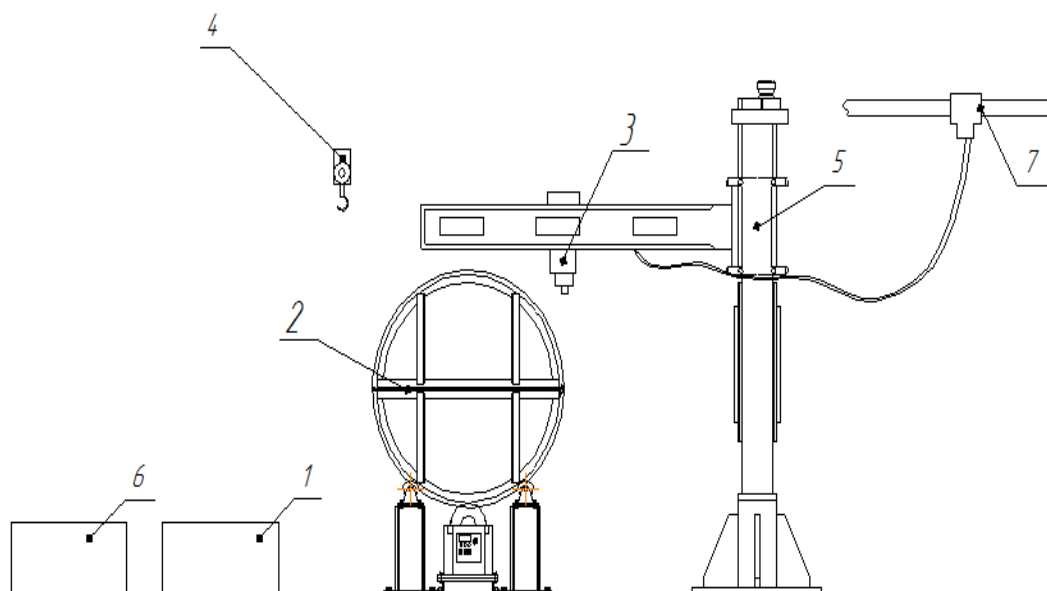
Схема компоновки рабочего места сварки подузла №3:
